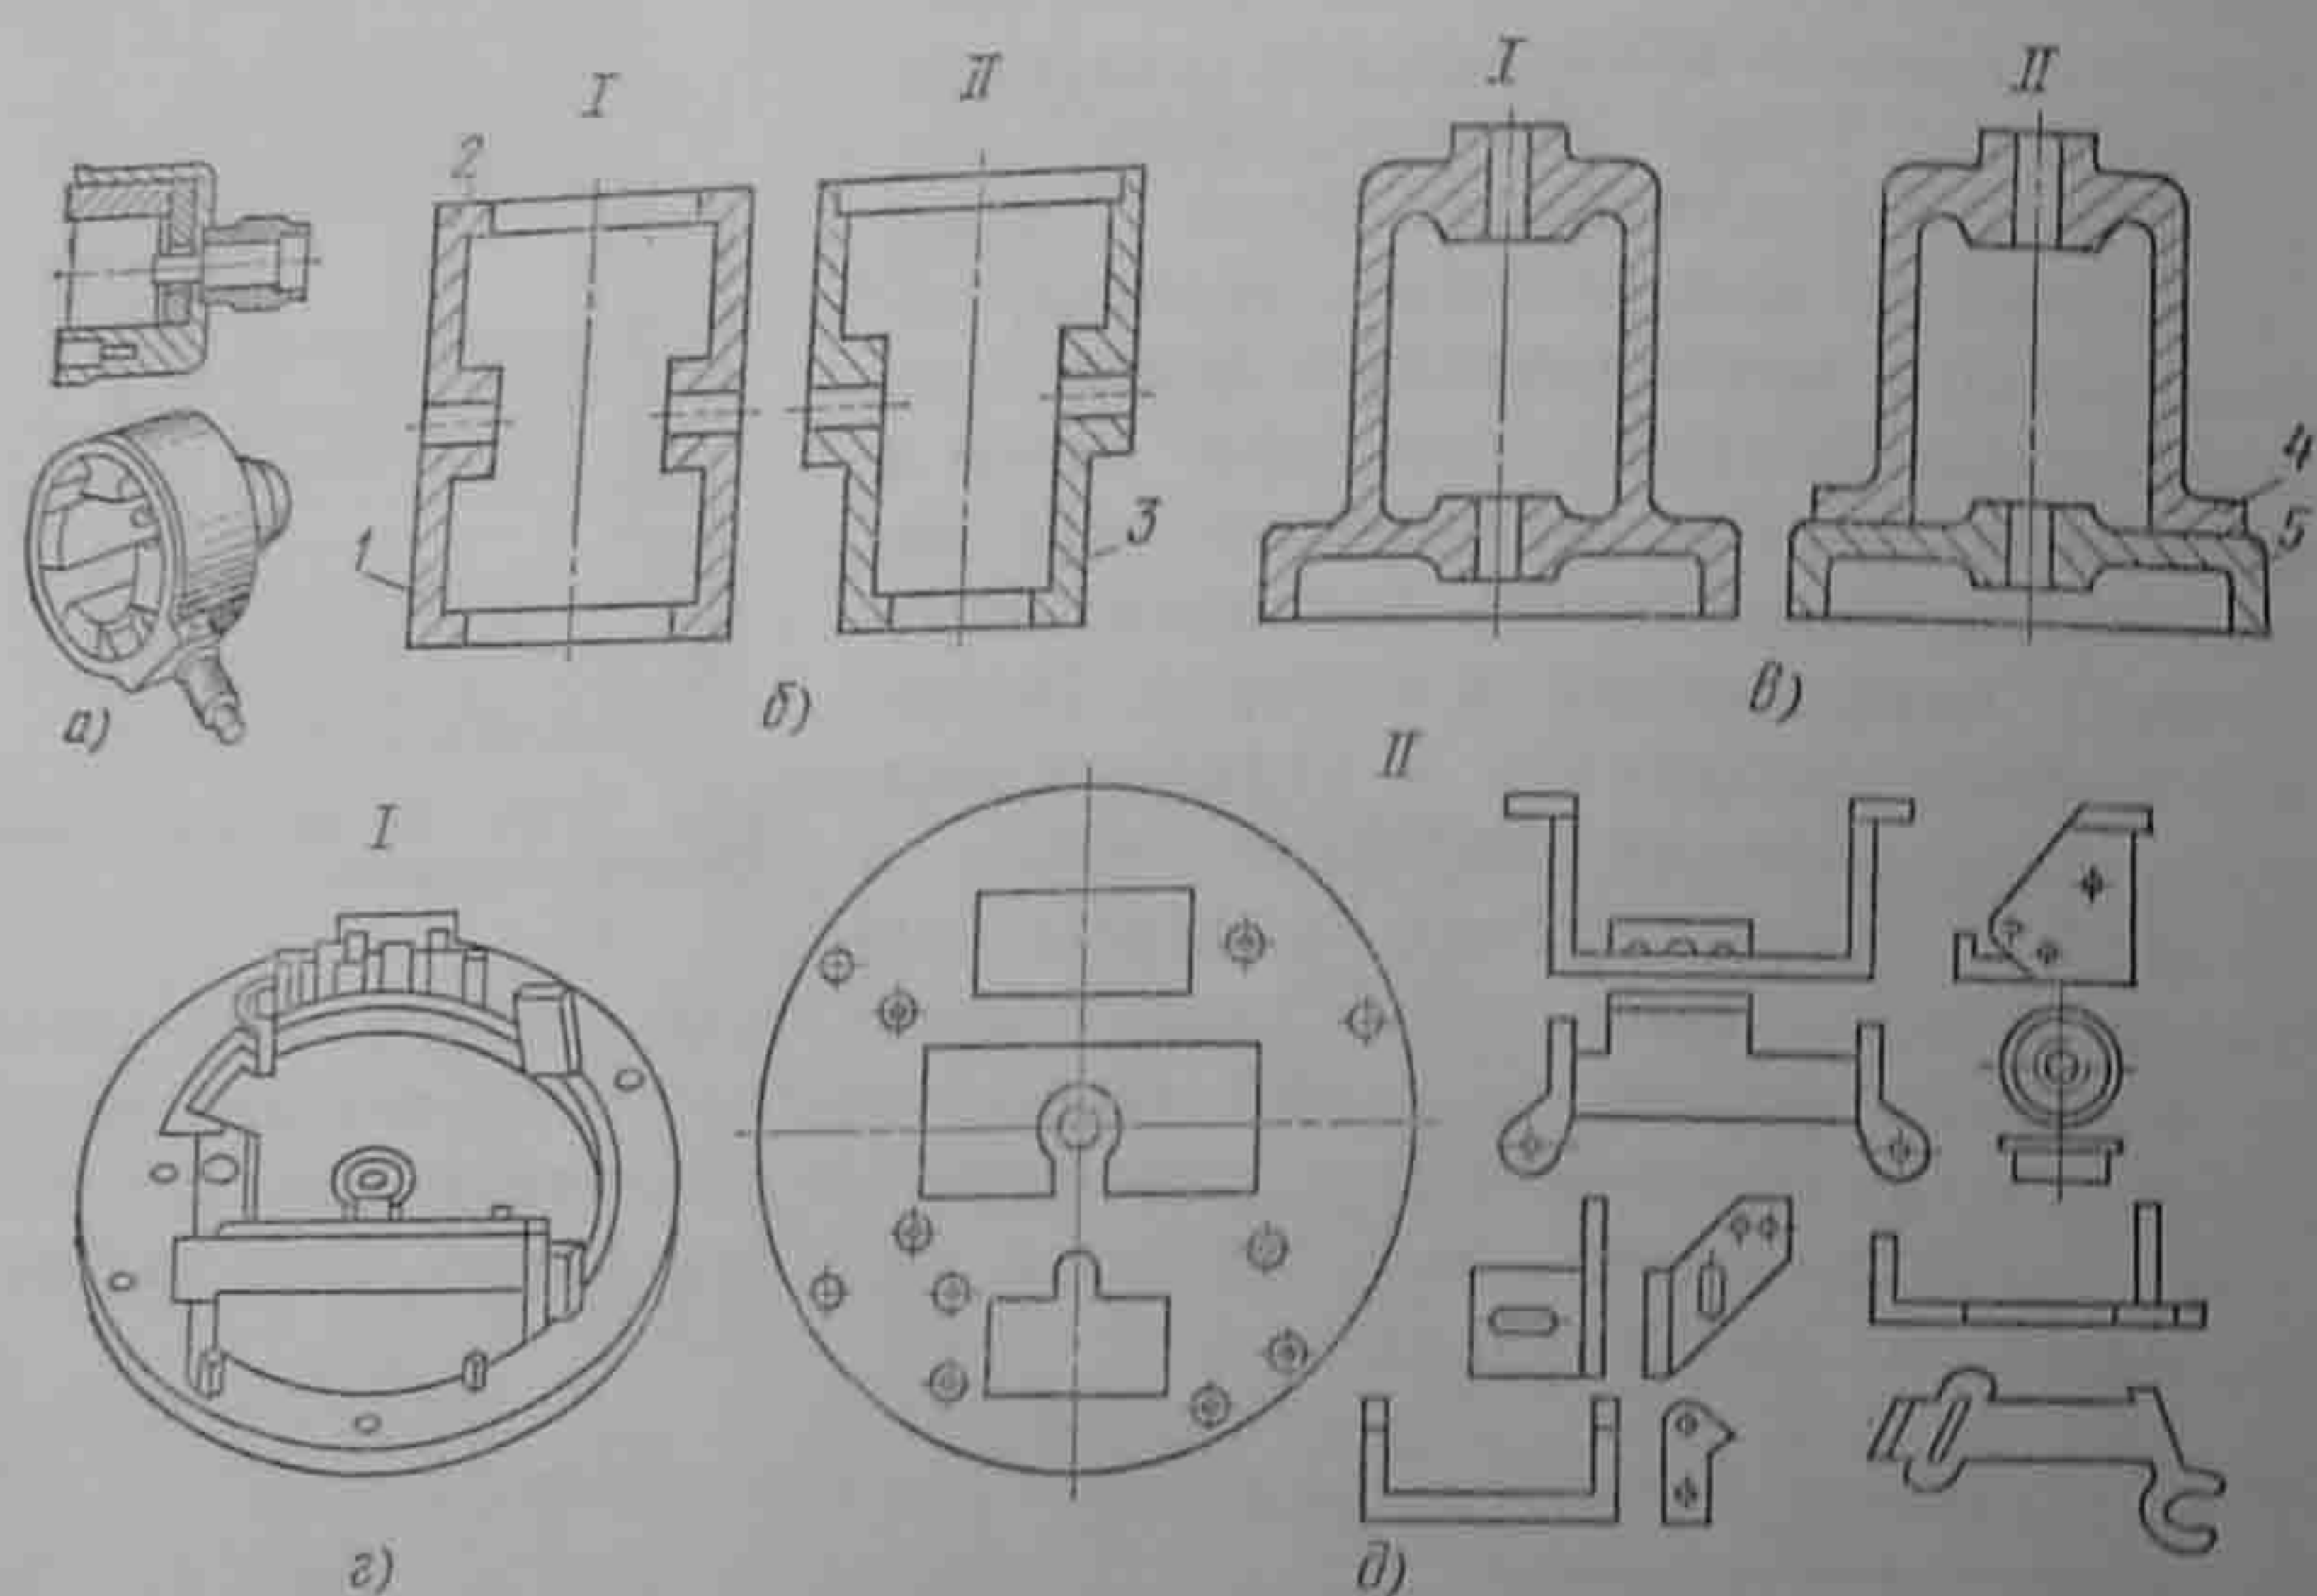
Изменение конструкции литой детали для облегчения ее изготовления: I — первоначальная конструкция отливки; II — измененная конструкция отливки
